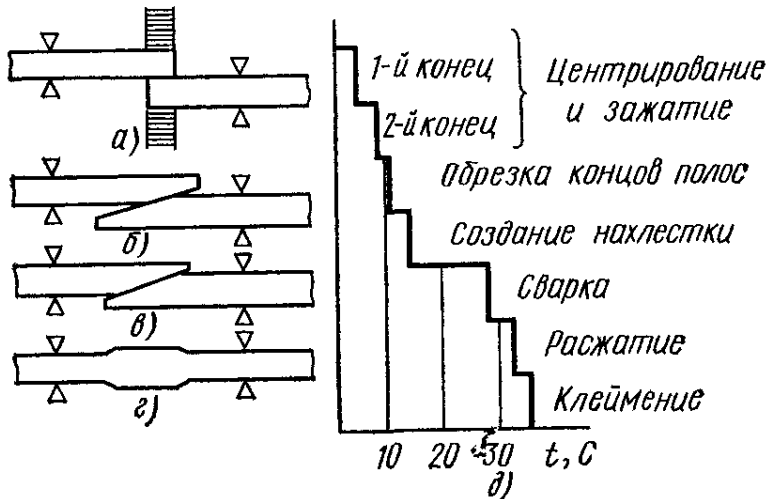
Схема сварки с предварительным холодным раздавливанием (а, б, в, г) и циклограмма подготовки к сварке и сварка (д)
